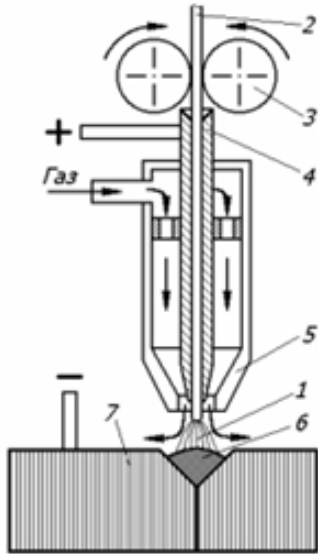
Полуавтоматическая сварка плавящимся электродом в струе защитного газа: 1 – электрическая дуга; 2 – сварочная проволока; 3 – ролики механизма подачи проволоки; 4 – токопровод; 5 – сопло; 6 – свариваемый шов; 7 – изделие.
